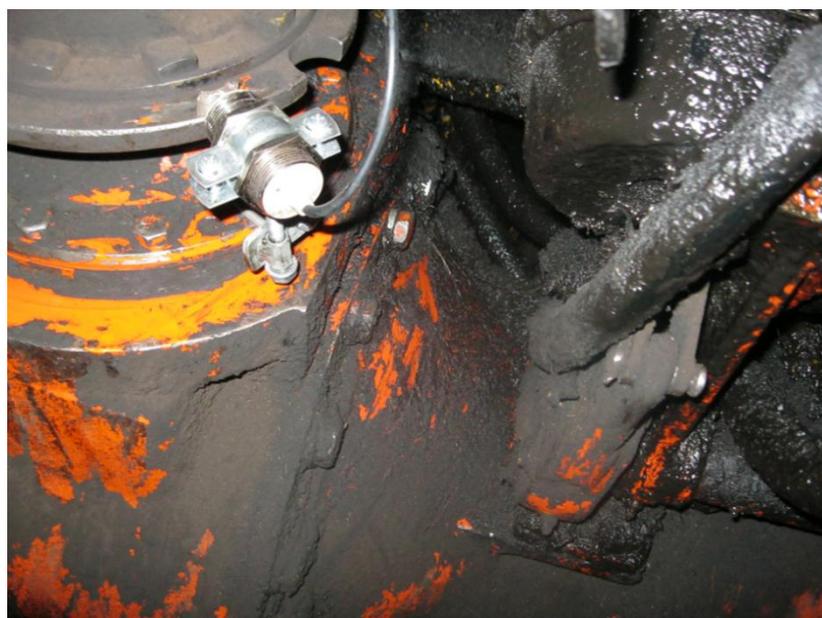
Установка датчика оборотов хвостовика вала ведущего моста
